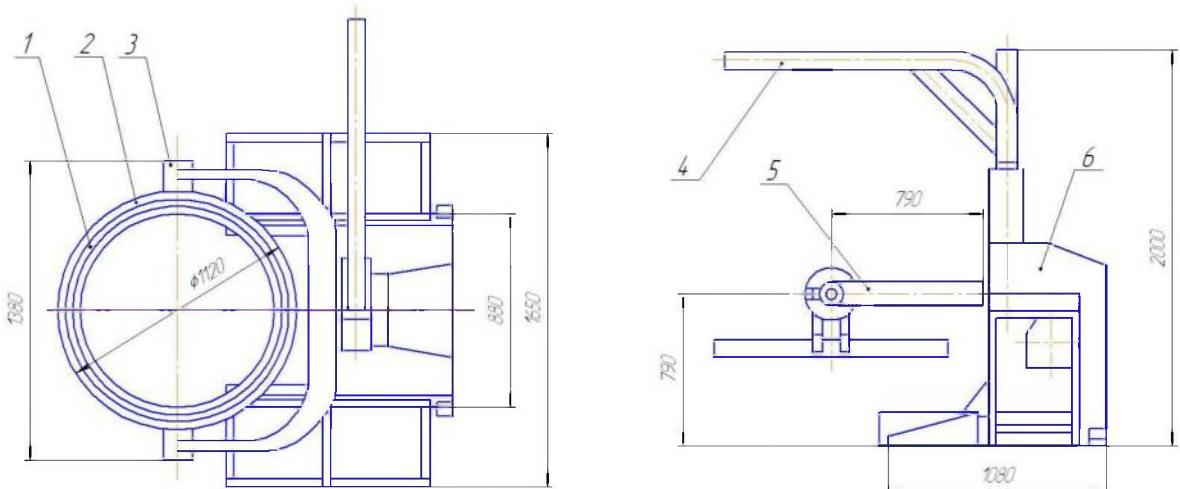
Стенд для разборки и сборки V- образных двигателей (Модель 6501-72)
